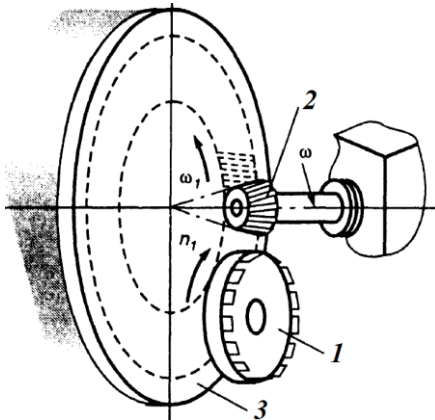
Робочі рухи верстата для нарізання коліс зі спіральним зубом
